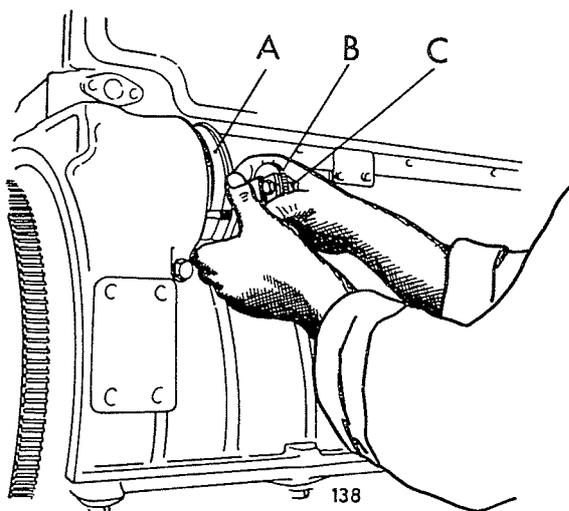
Einbau des Einspritzpumpenantriebes F/A 4-6L 514
